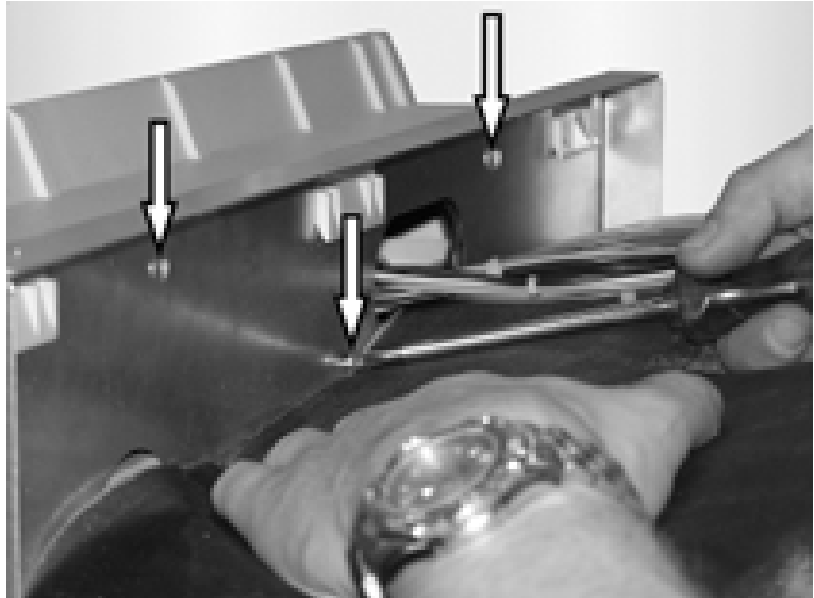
Das Kesselschaltfeld (ohne Regelung) von der Rückseite des vorderen Verkleidungsbleches mit drei Blechschrauben befestigen.
